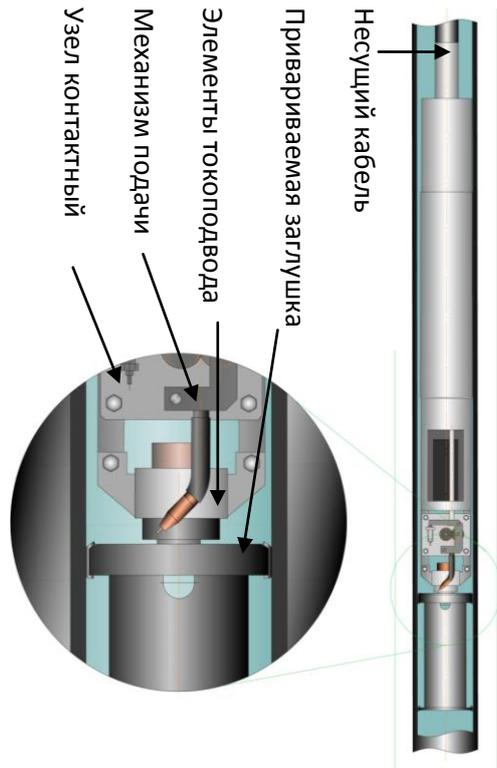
Автомат для глубоководной подводной сварки мокрым способом
